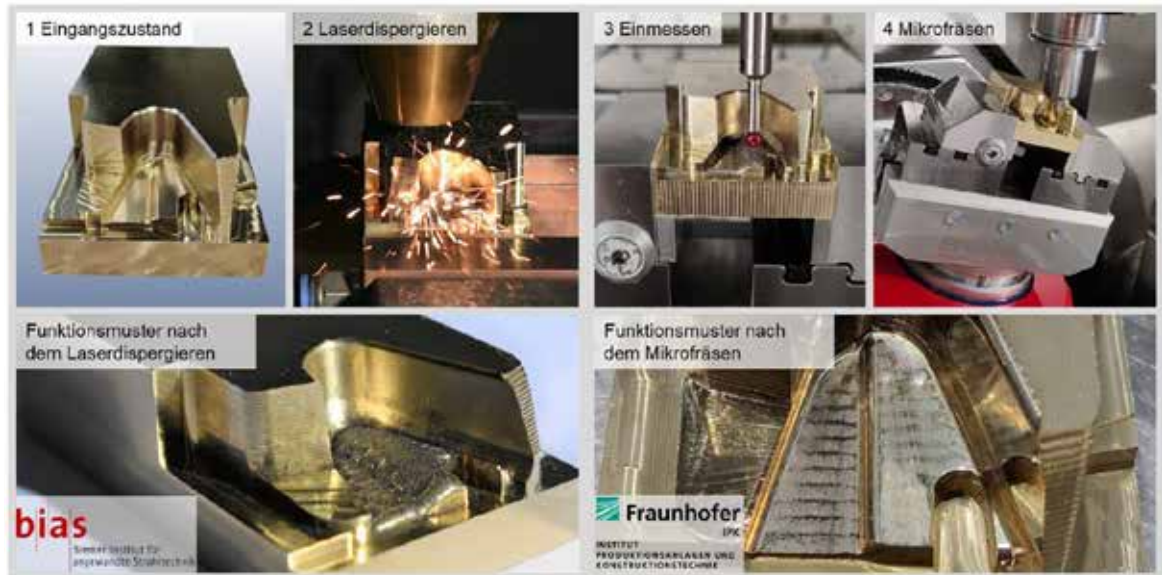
• Prozesskette für die Herstellung eines Spritzgusswerkzeugs mit einer MMC-Oberfläche.
